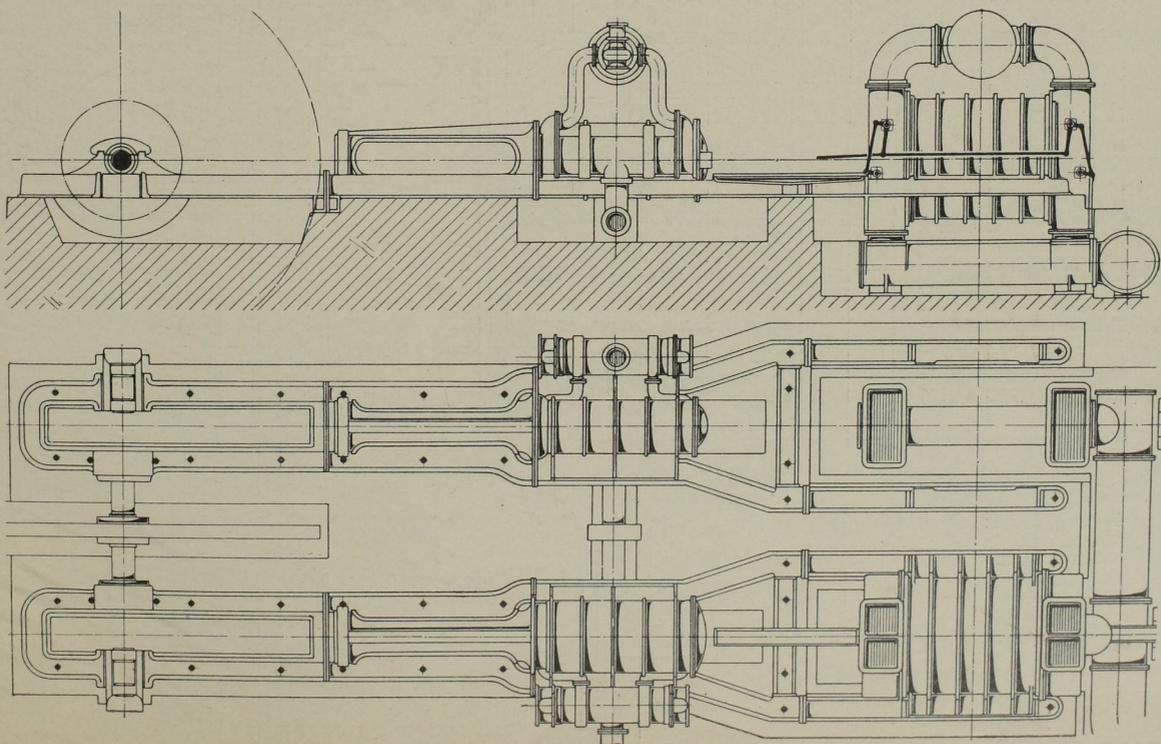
Grundriss und Aufriss der Gesamtanordnung. Massst. 1:125.
